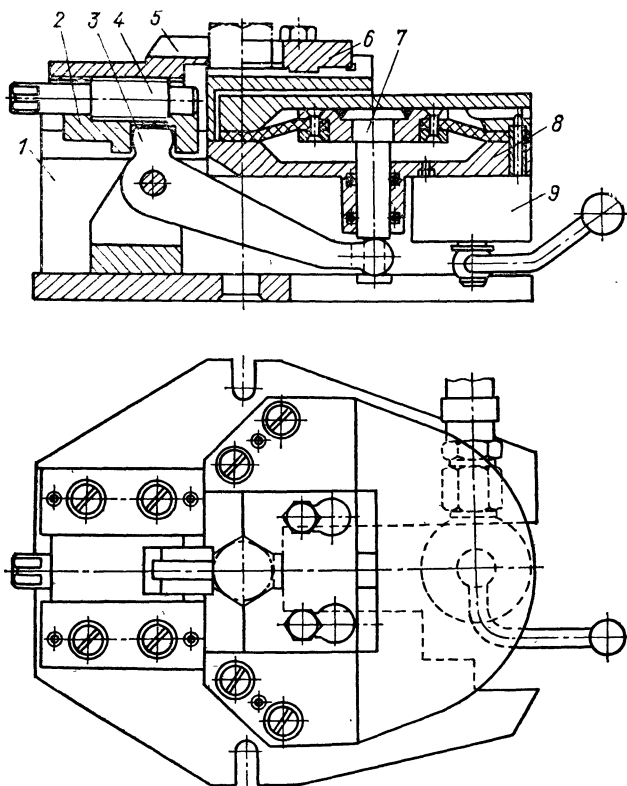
Специализированное наладочное приспособление с приводом от пневмокамеры для фрезерования пазов и шлицев в мелких деталях
